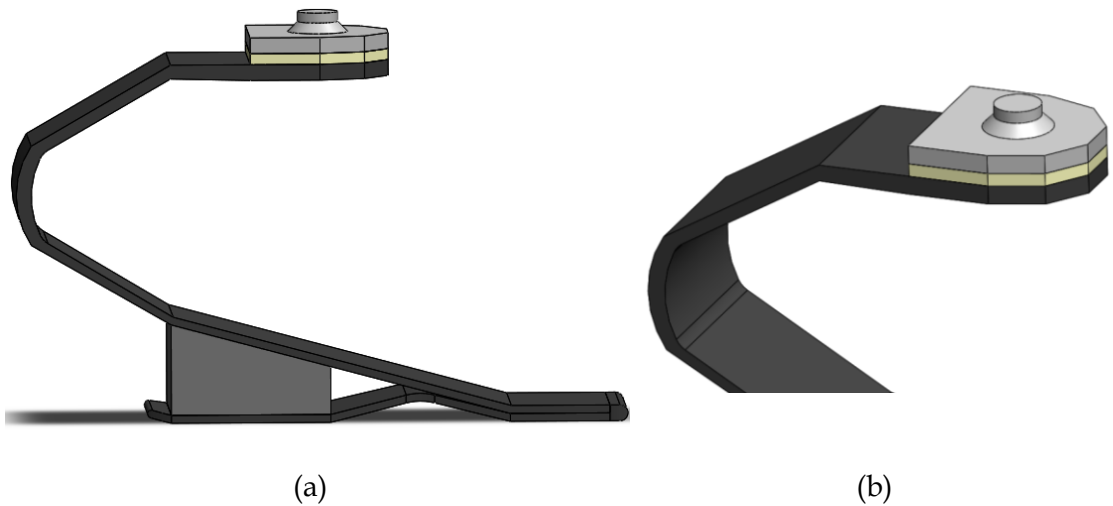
Vista laterale dell'intera struttura (a) e zoom sulla parte superiore (b) del CAD del piede protesico
